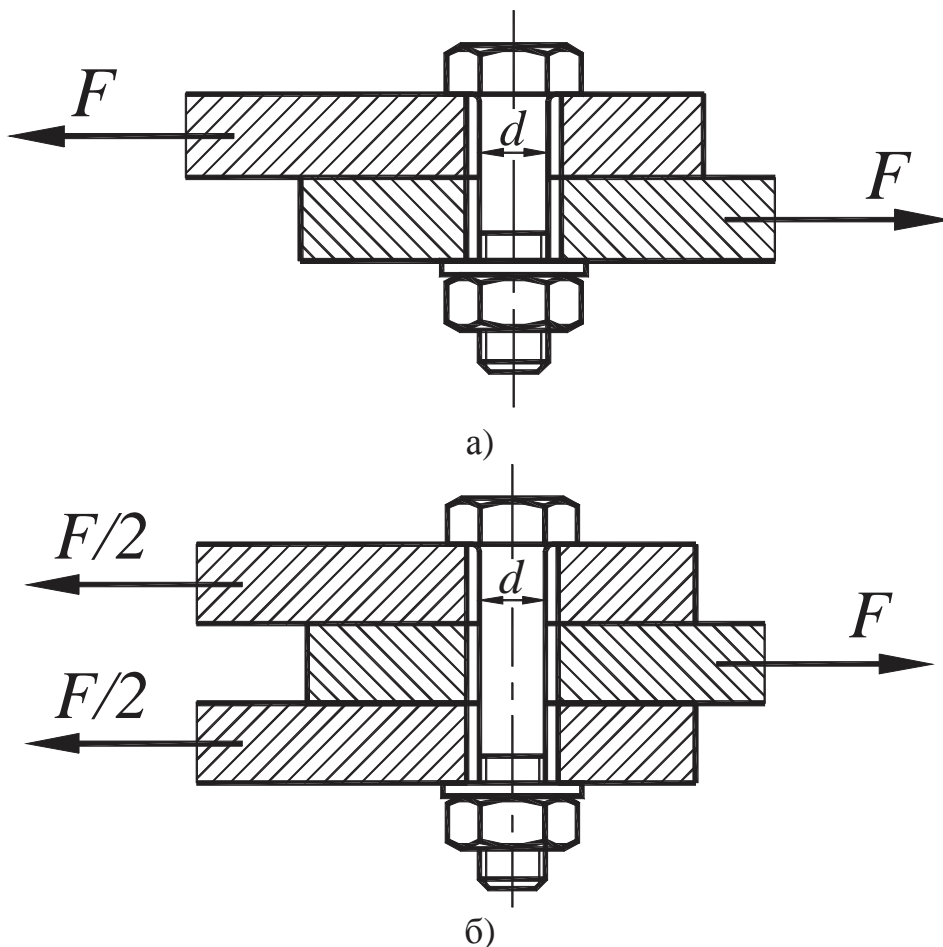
Розрахункова схема болтового з'єднання з зазором
